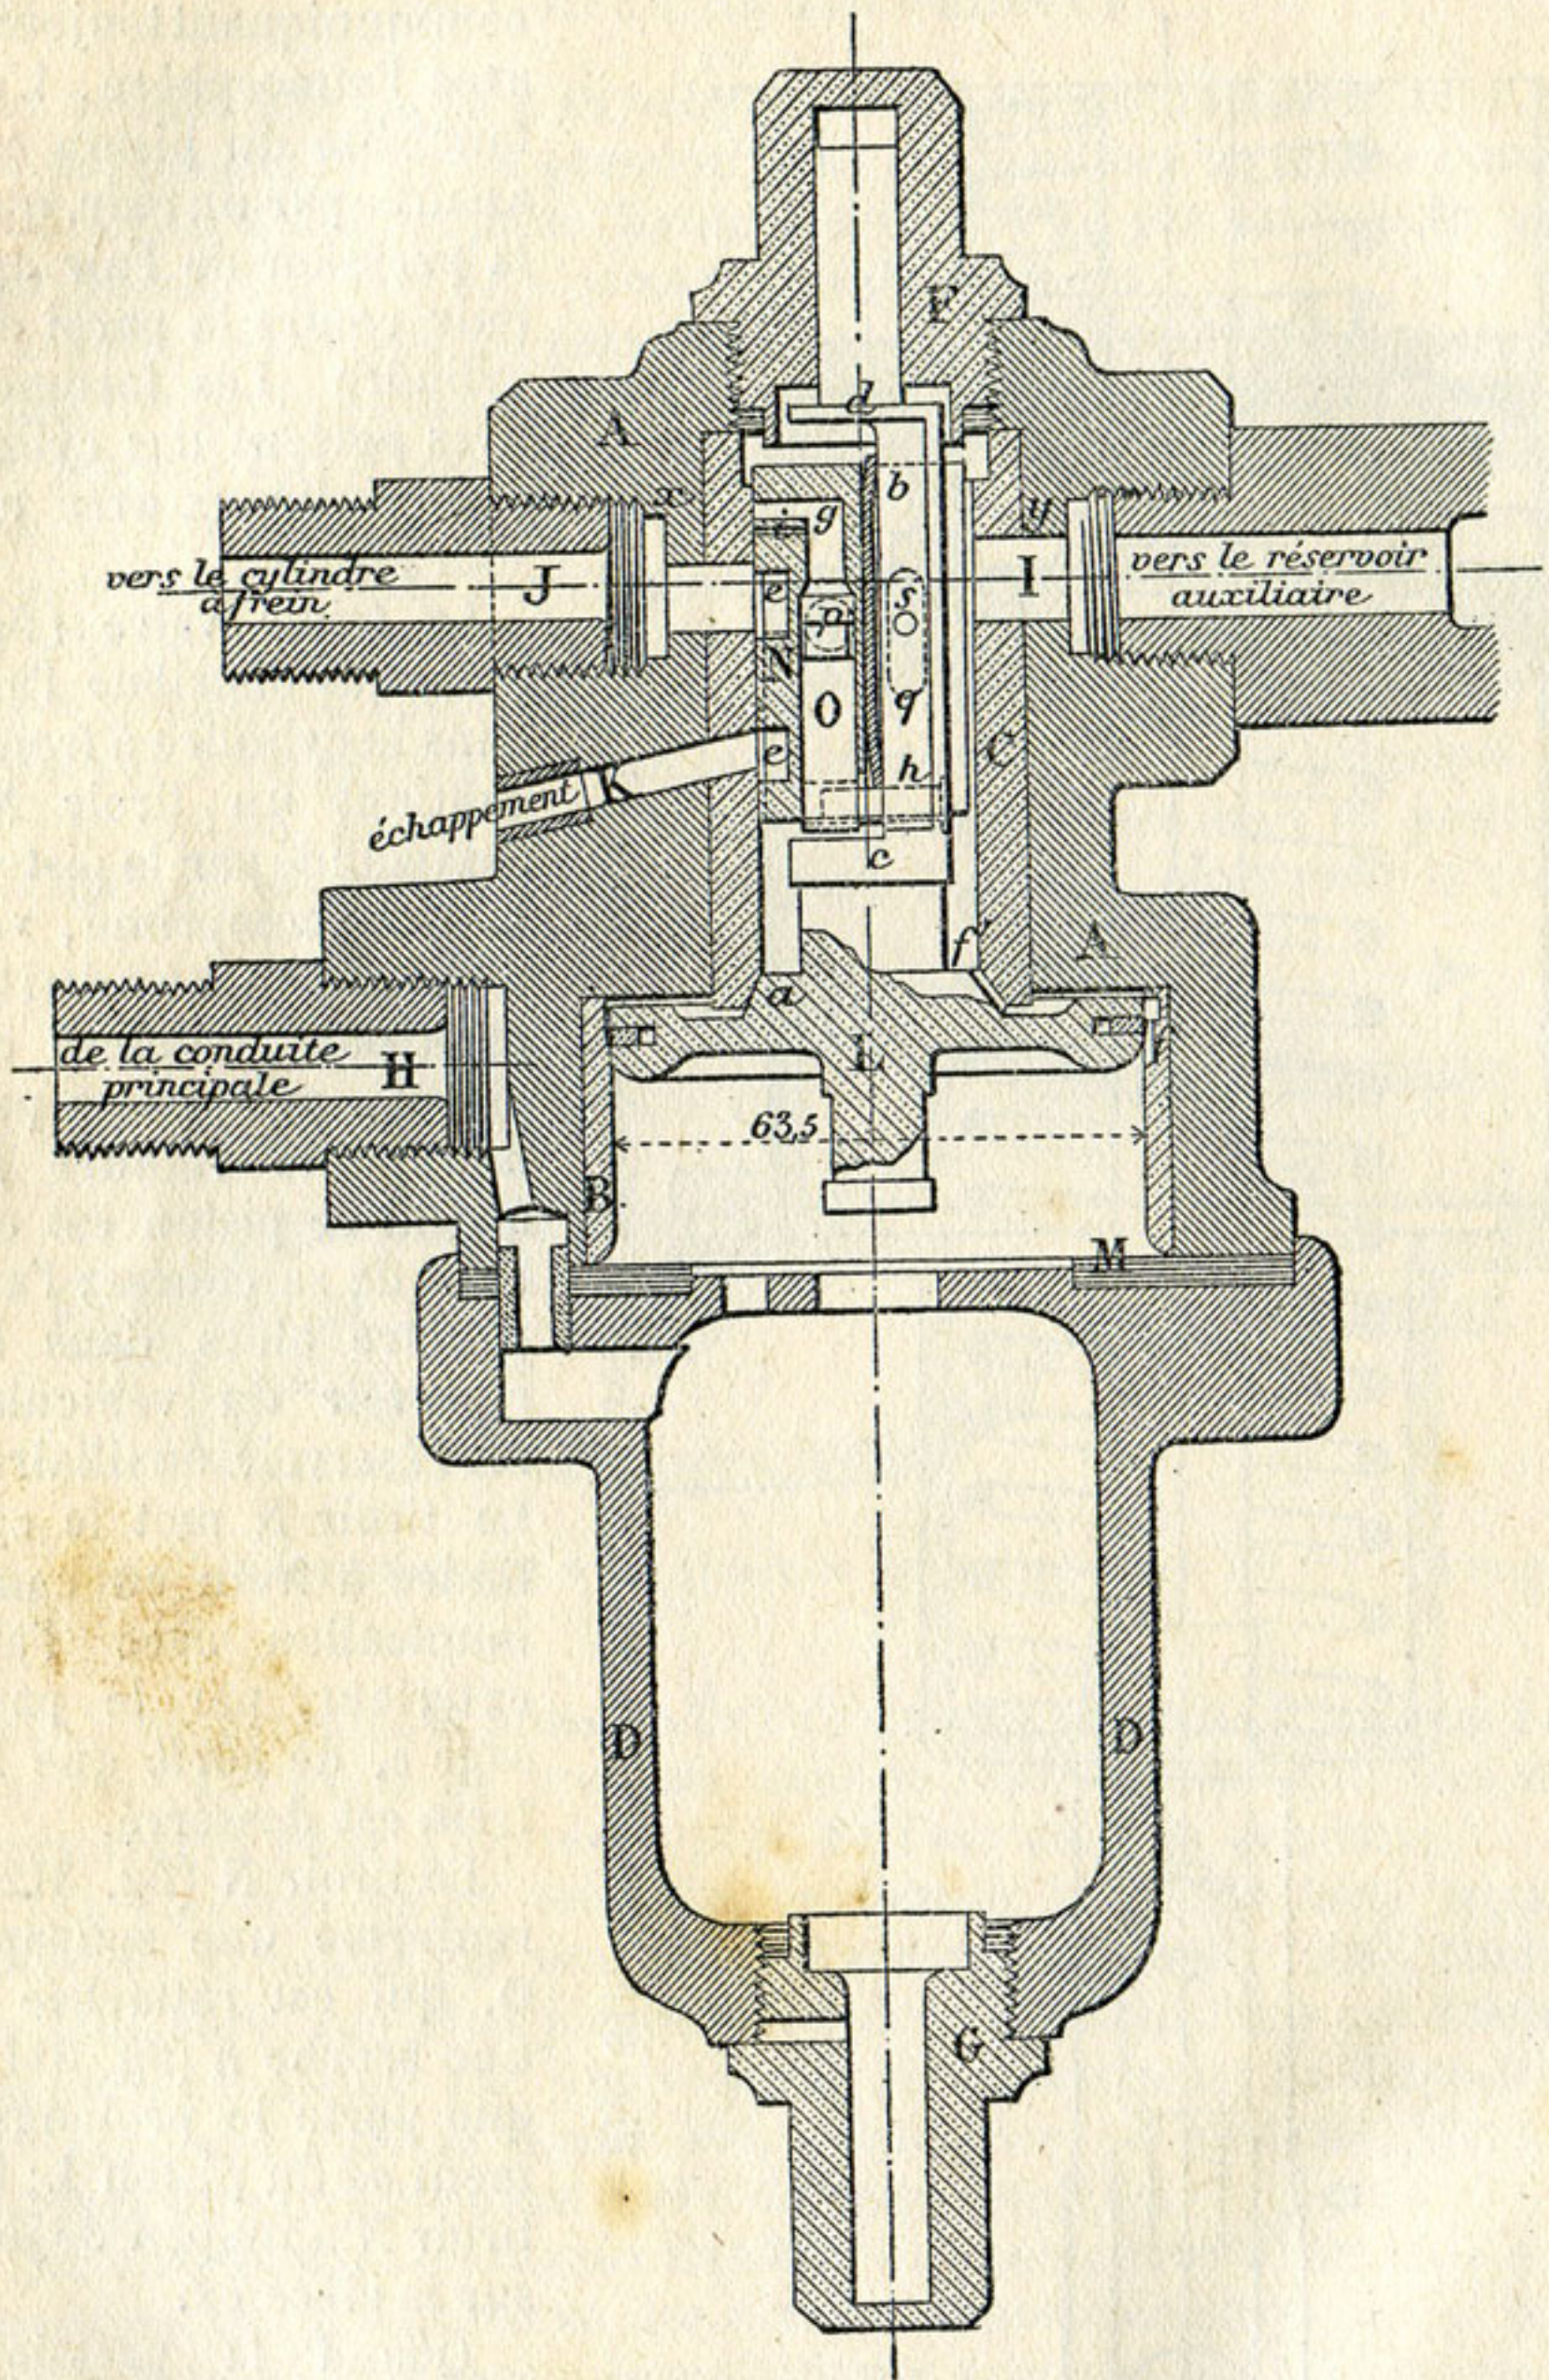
Triple valve du frein Westinghouse : L, piston, commandant le tiroir N par la pièce *cd*, qui laisse un peu de jeu : en descendant, le piston ouvre d'abord la soupape O, que porte le tiroir.
